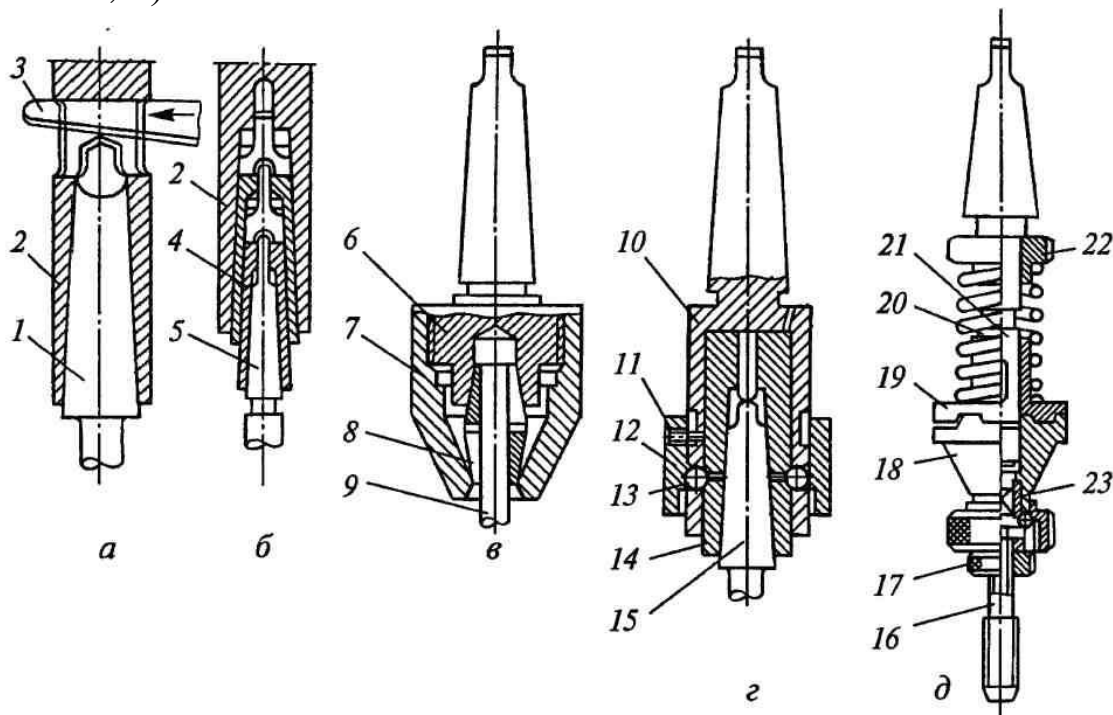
Устройства для закрепления осевого инструмента на сверлильных станках: а – с большим коническим хвостовиком; б – с малым коническим хвостовиком; в – с цилиндрическим хвостовиком; г – быстросменный патрон; д – реверсивный патрон; 7, 17 и 22 – гайки; 1, 5, 9 и 15 – хвостовики инструмента; 2 – шпиндель станка; 3 – клин; 4 – переходная втулка; 6, 10 – корпус патрона; 8 – цанга; 11 – стопорный винт; 12 – кольцо; 13 – шарики; 14, 23 – сменные втулки; 16 – метчик; 18, 19 – полумуфты; 20 – пружина; 21 – оправка; 3 – клин
